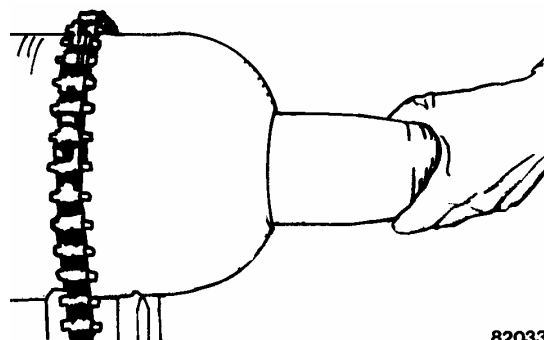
DESMONTAJE DEL ANILLO ANTI-EXTRUSION
